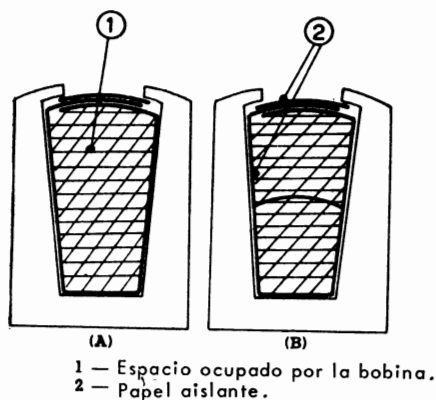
Colocación del papel aislante en las ranuras de los devanados.
